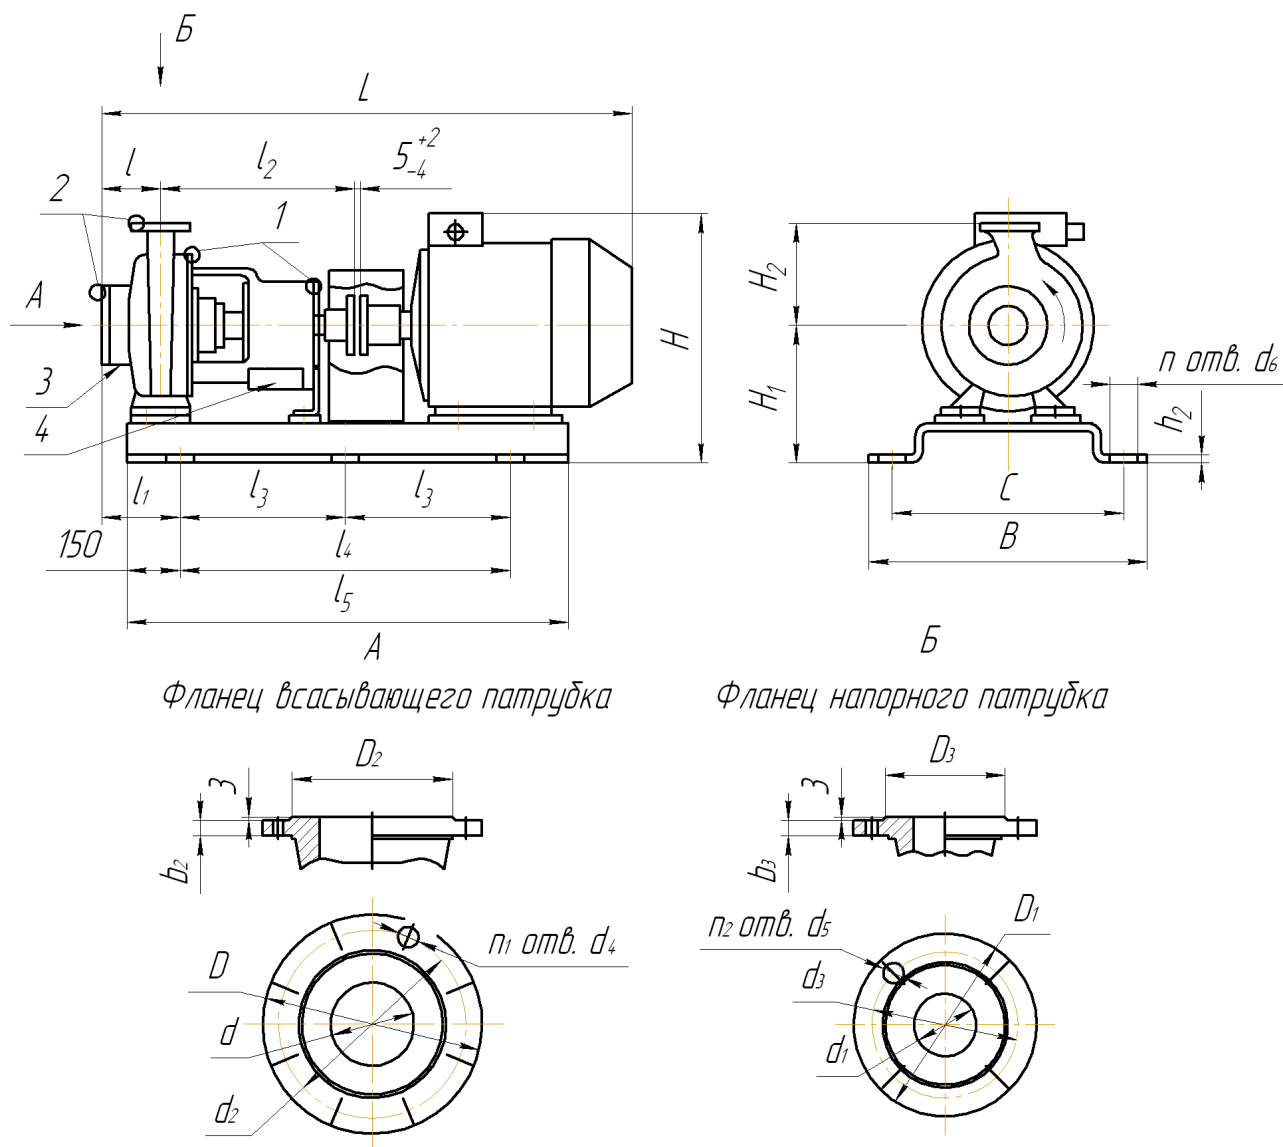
Габаритные и присоединительные размеры агрегатов типа «АХ» и «АХО»
